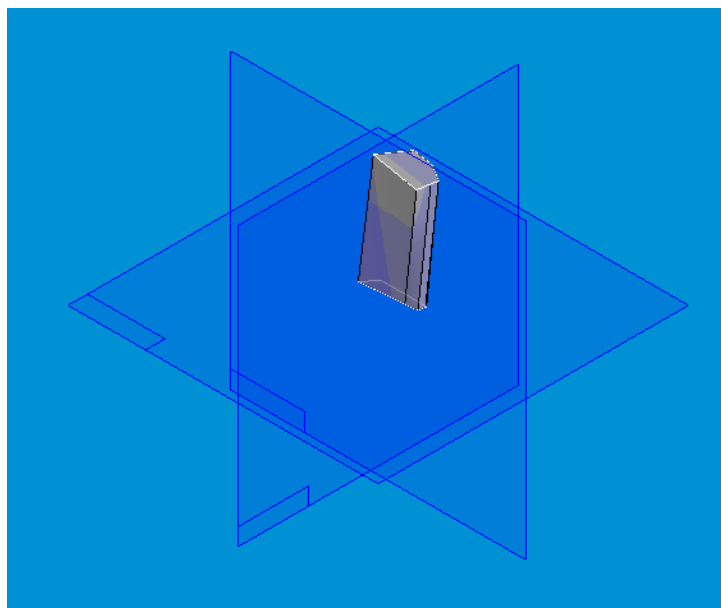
Ricostruzione geometrica del pilastro 19.
